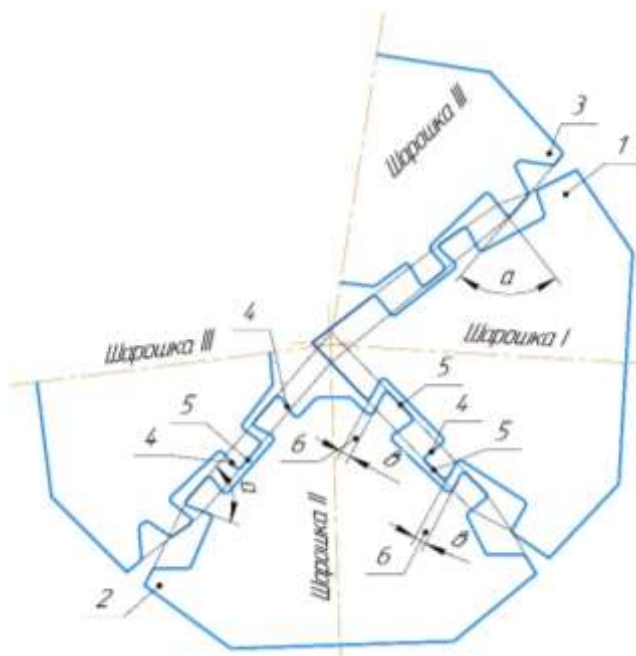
а – Схема вооружения самоочищающихся шарошек с коэффициентом перекрытия забоя равным единице;
